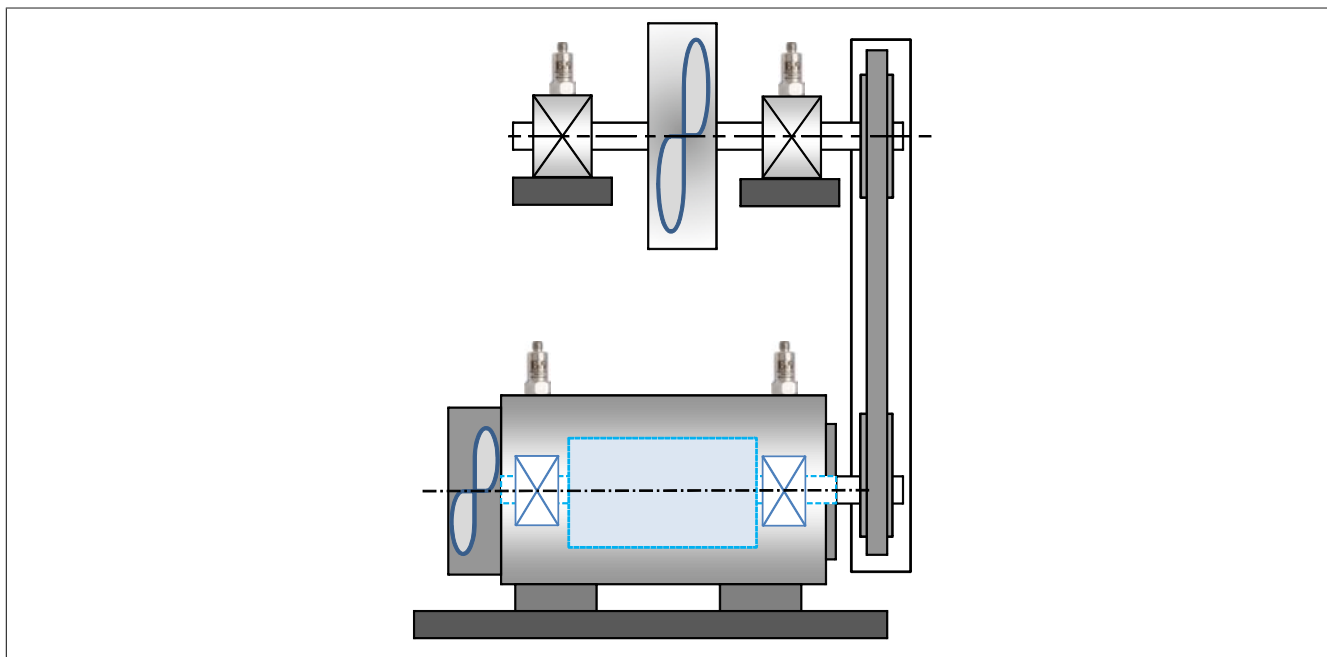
Systemskizze - Aufbau eines Ventilators mit Riemenantrieb - alternative Lagerung
